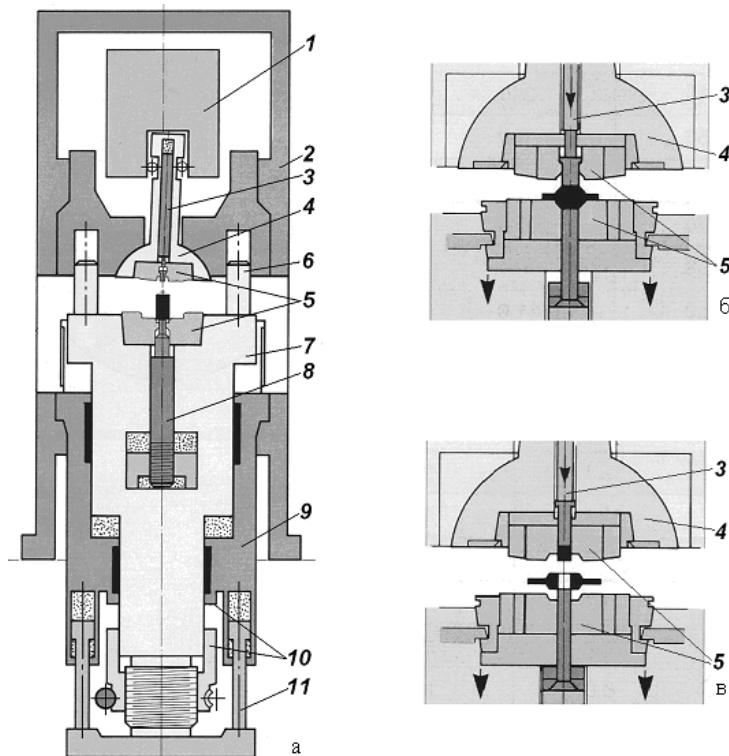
Конструктивна схема преса для ШСО моделі Т-630 (а) і технологічні варіанти використання приводного пуансона для выталкивания детали из верхней полости штампа (б) или прошивки центрального отверстия (в) (где: 1 – привод механизма обкатывания; 2 – станина; 3 – верхний приводной пуансон; 4 – активный прессователь; 5 – инструмент; 6 – направляющие; 7 – ползун; 8 – нижний выталкиватель; 9 – корпус гидроцилиндра; 10 – упор; 11 – возвратные цилиндры)
